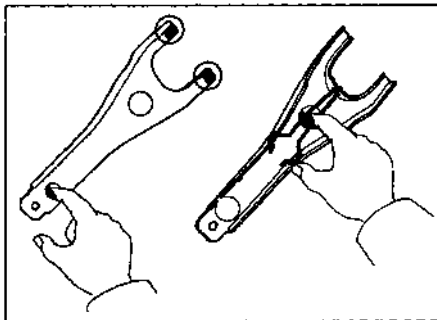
Нанесите немного тугоплавкой смазки на рабочие поверхности вилки сцепления
